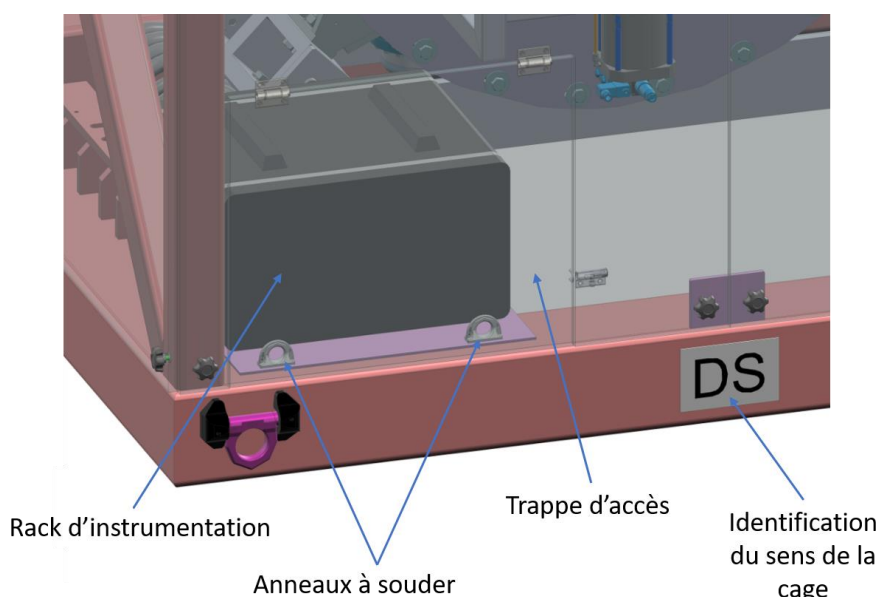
Trappe d'accès pour les racks d'instrumentation.
